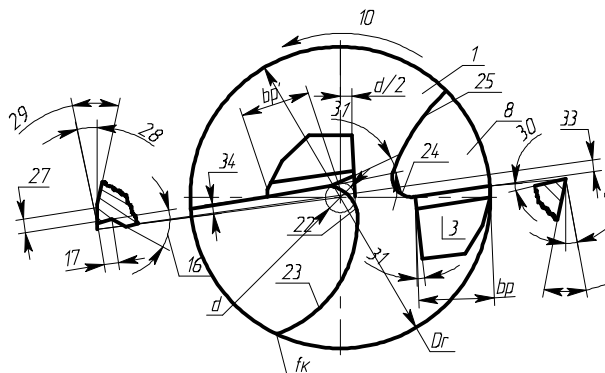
Вид на резцовую головку по стрелке К с исполнением 5 корпуса.
